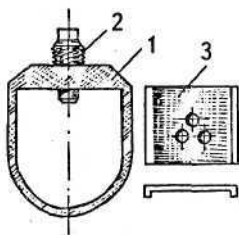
Приспособление для крепления ножа и регулирования захвата косы:
